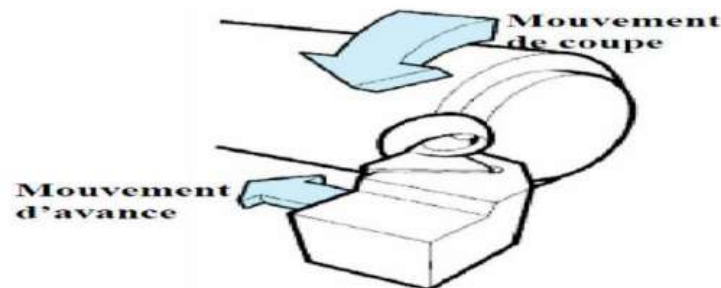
Mouvements de coupe et d'avance en tournage [3].
